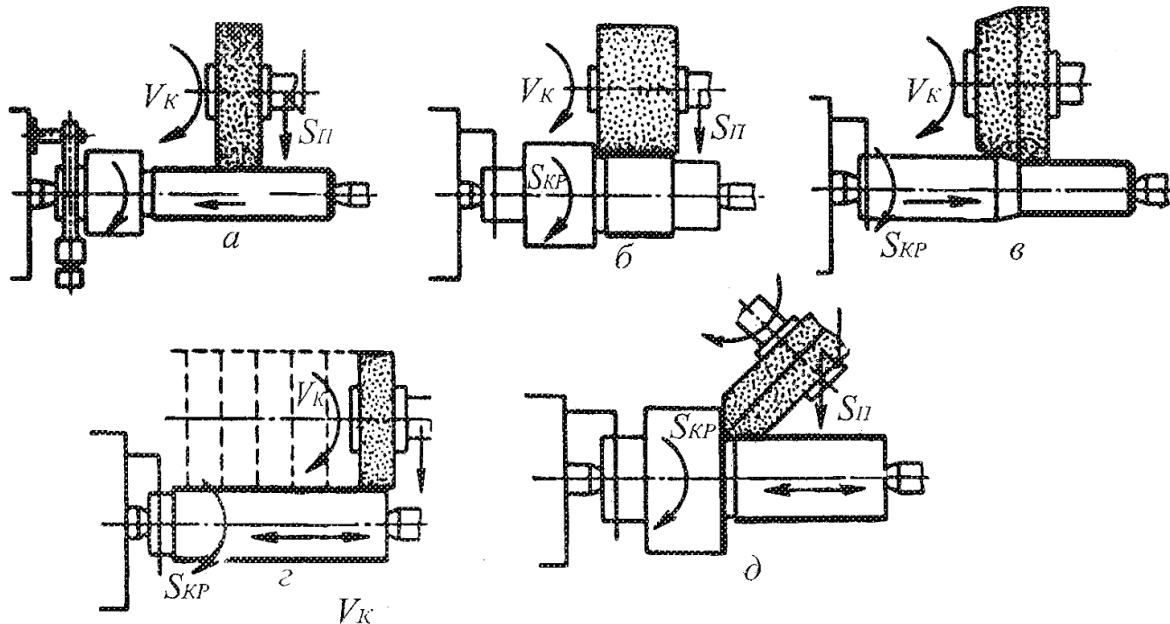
Схеми обробки заготовок на круглошліфувальних верстатах
